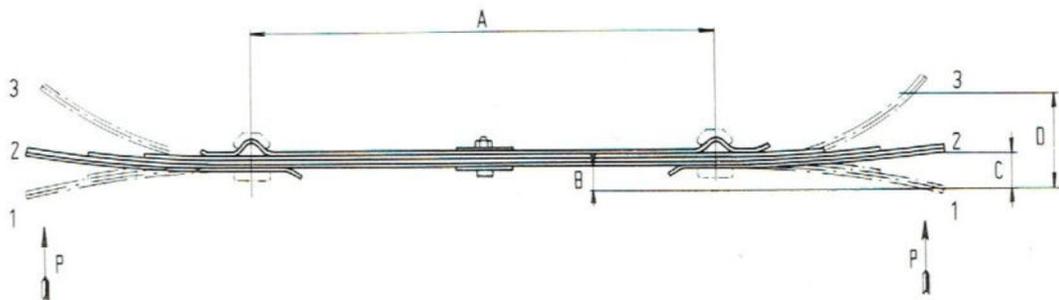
Prüfwerte der Blattfeder (bei wie im Fahrzeug eingespannter Feder).
